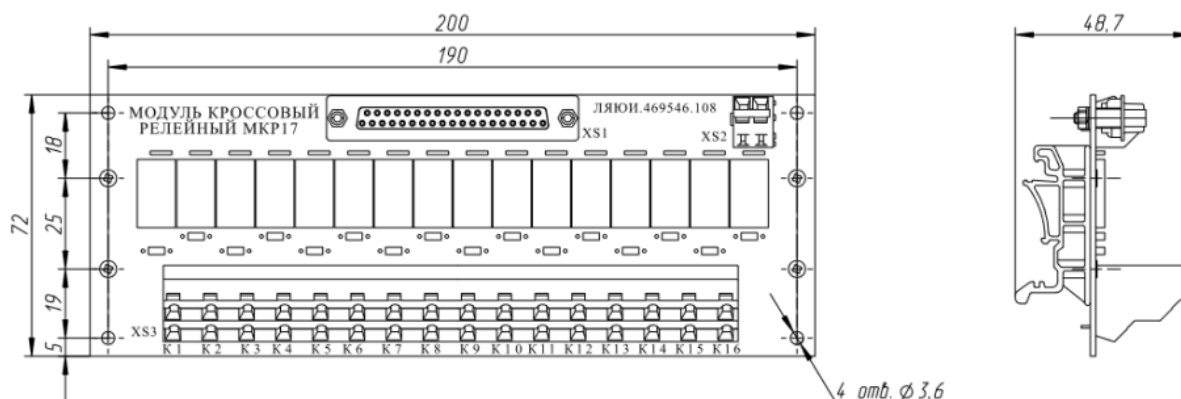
Сборочный чертеж модуля кроссового релейного МКР17
